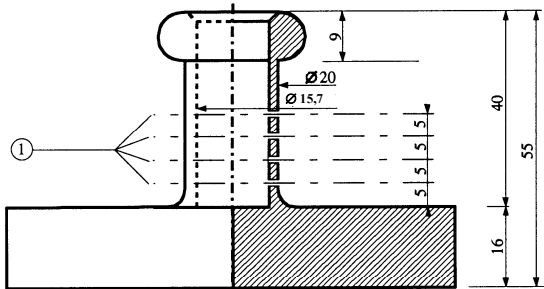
Полый бронзовый цилиндр, закрытый с одной стороны; чертеж и размеры детали в мм
